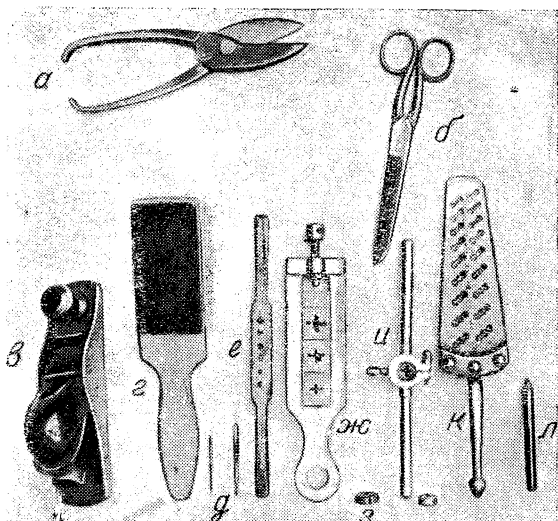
а — ножницы по металлу, б — обычные ножницы, в — малый рубанок, г — кардошетка, д — метчики, е — вороток для метчиков, ж — клуппик с тремя плашками, з — плашка, и — клуппик с вставными плашками, к — винторезная доска, л — керн
